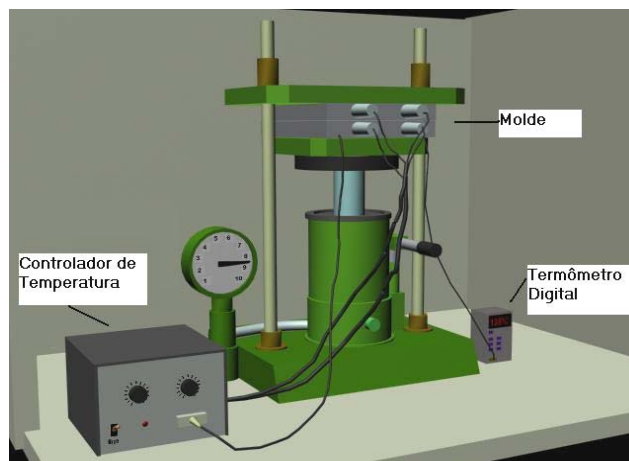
Representação do sistema utilizado para a moldagem por compressão.
